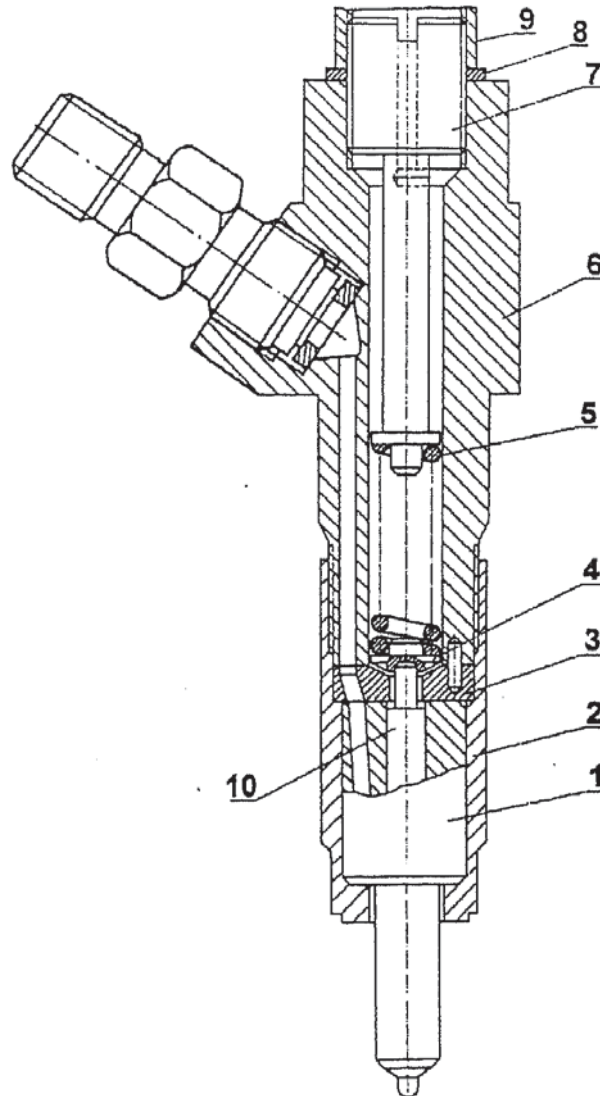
Опытная форсунка конструкции НЗТА: 1 — распылитель; 2 — накидная гайка; 3 — проставка; 4 — штанга; 5 — пружина; 6 — корпус форсунки; 7 — регулировочный винт; 8 — контргайка; 9 — колпак; 10 — игла распылителя
